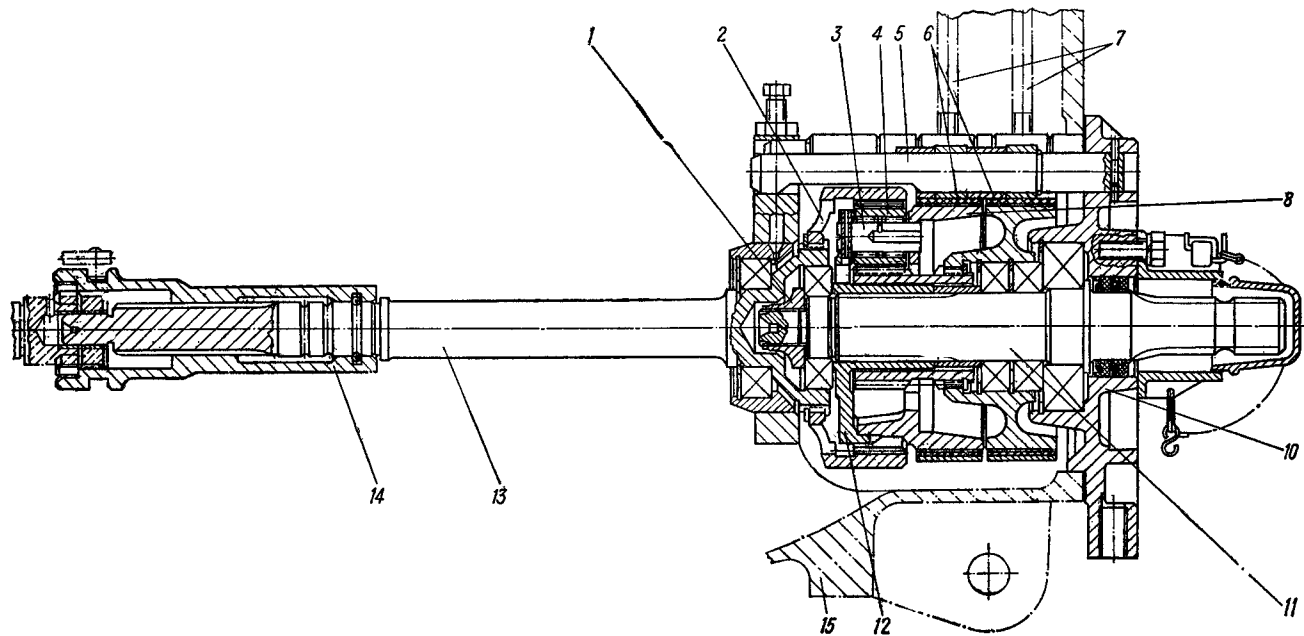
Планетарный редуктор заднего вала отбора мощности:
